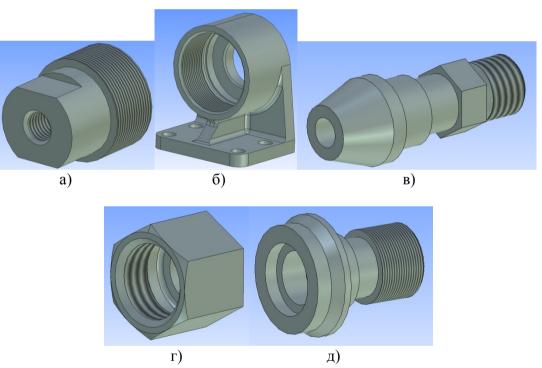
Трехмерные модели деталей сборочного узла: а — корпус; б — крышка; в — ниппель; г — гайка; д — штуцер
